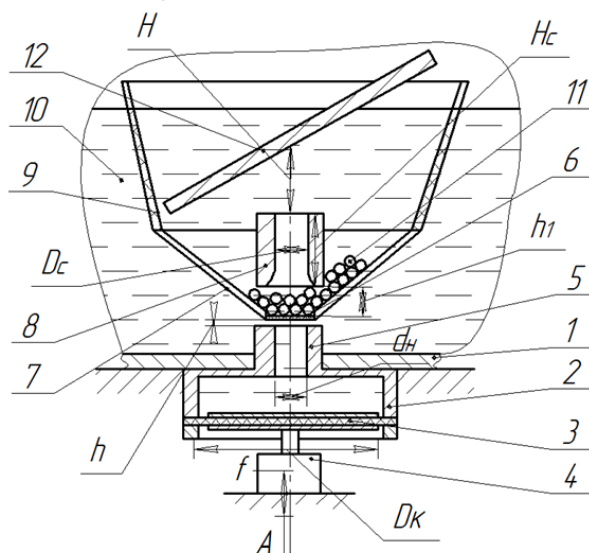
Схема роботи вібраційної машини для очищення та мийки деталей машин у пульсуючому потоці рідини з твердими частинками: 1 – корпус ванни; 2 – камера пульсації; 3 – мембрана з дисками; 4 – вібропривід; 5 – насадок; 6 – сітка; 7 – короб для збору твердих частинок; 8 – сопло; 9 – сітка; 10 – м'яка рідина; 11 – тверді частинки; 12 – поверхня, що очищується; H – відстань від сопла до поверхні, що очищується; H_c – висота сопла; h – відстань від насадка до сітки; h_1 – відстань від сітки до сопла; d_n – діаметр насадка; D_k – діаметр камери пульсації; D_c – діаметр сопла; f – частота коливань віброприводу; A – амплітуда коливань віброприводу
